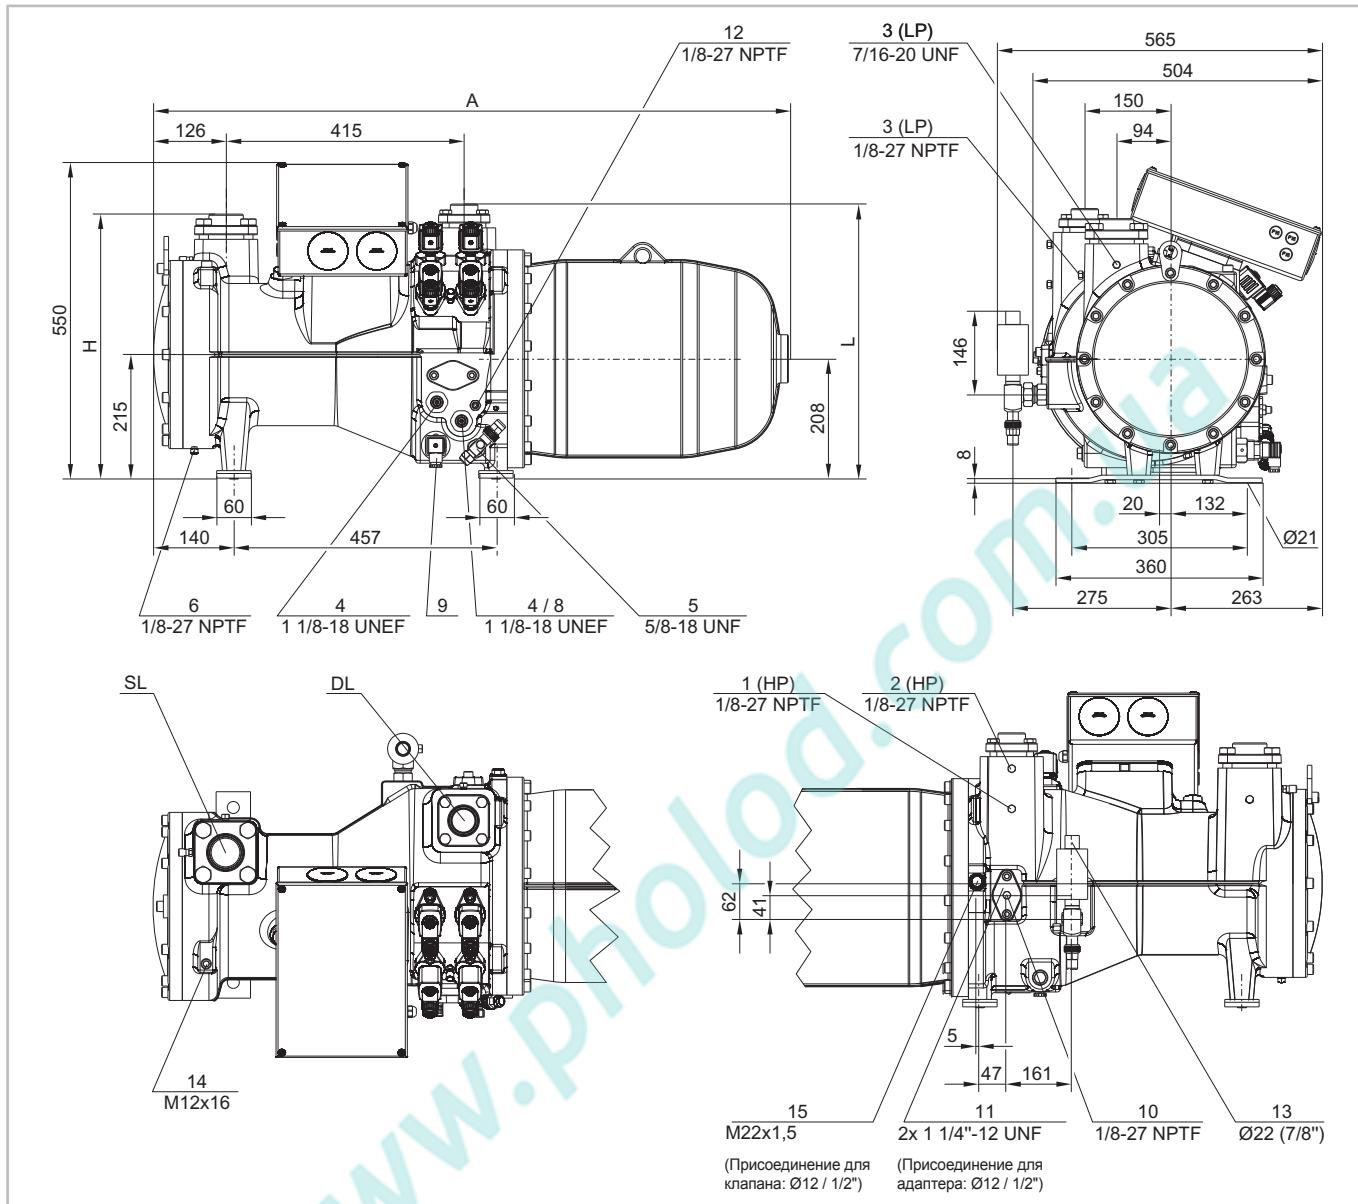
Чертежи с указанием размеров для компрессоров CSH6553-35Y .. CSH6593-60Y, CSK6151 .. CSK6161
